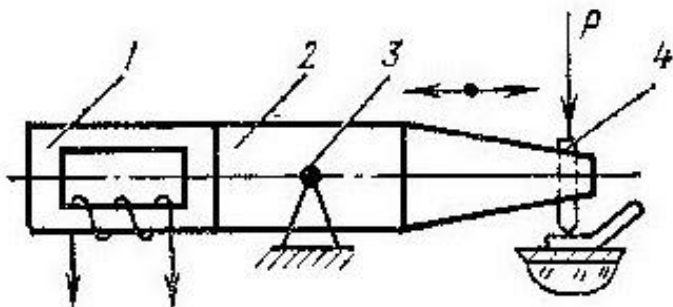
Схема ультразвуковой сварки: 1 – преобразователь;
